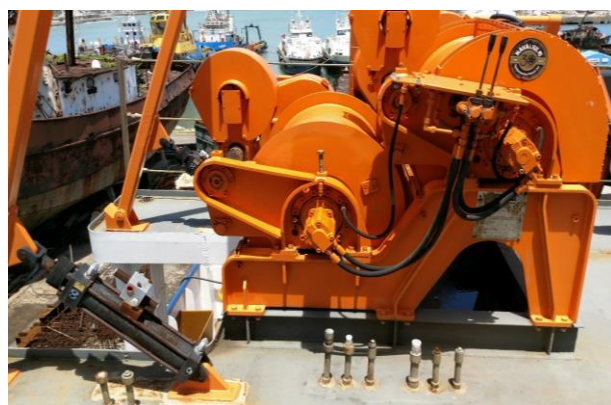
Guincho pistões s/ mangueiras e s/ teste
